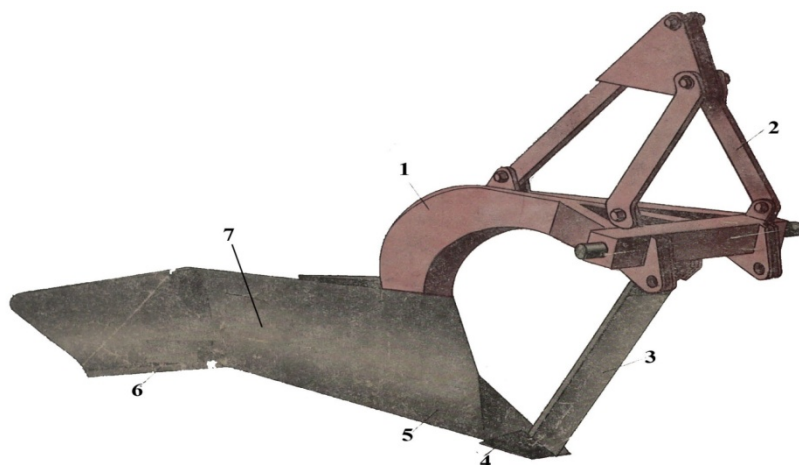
23 Корпус плуга ПЛО-400: 1 – стойка, 2- навесное устройство, 3 – черенковый нож, 4 – носок лемеха, 5 – лемех, 6 – бермоочиститель, 7 – отвал
